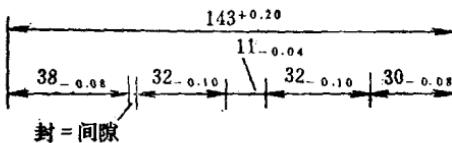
已知零件公差，求尺寸链封闭环尺寸和公差的实例
